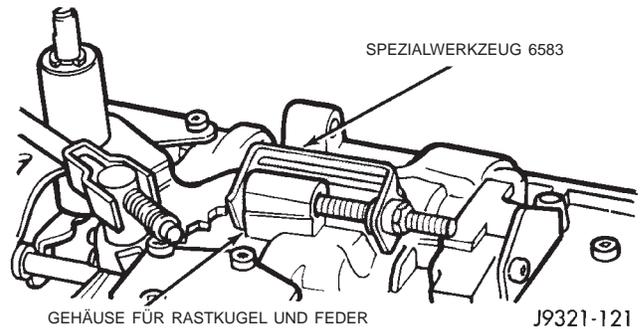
Rastkugel und Feder mit Haltewerkzeug fixieren
